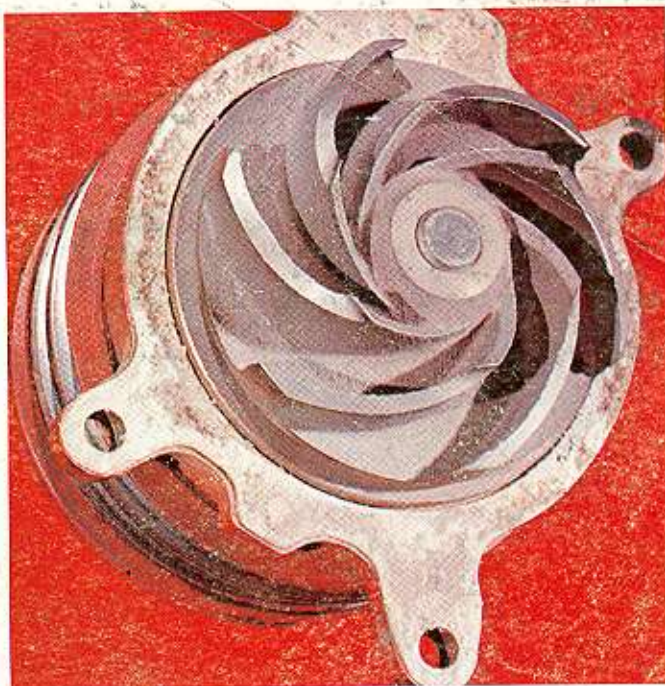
Bomba del agua que ha sufrido falla de un cojinete.
